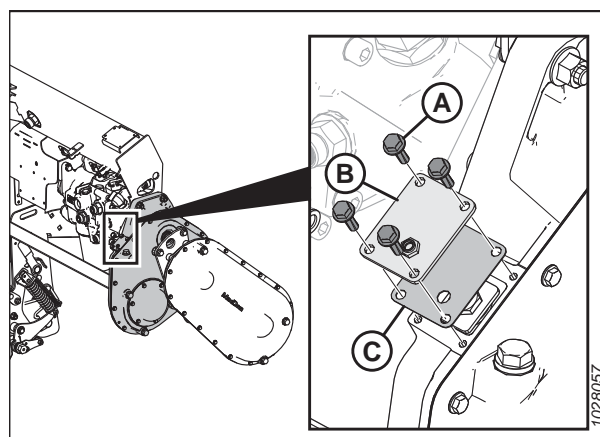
Hauptgetriebe mit Kettenspannerabdeckung
